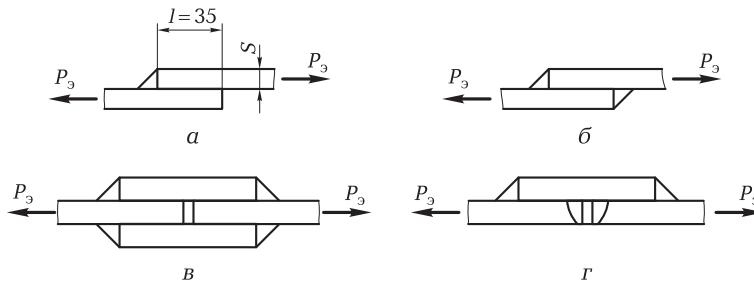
Нахлесточные сварные соединения:
